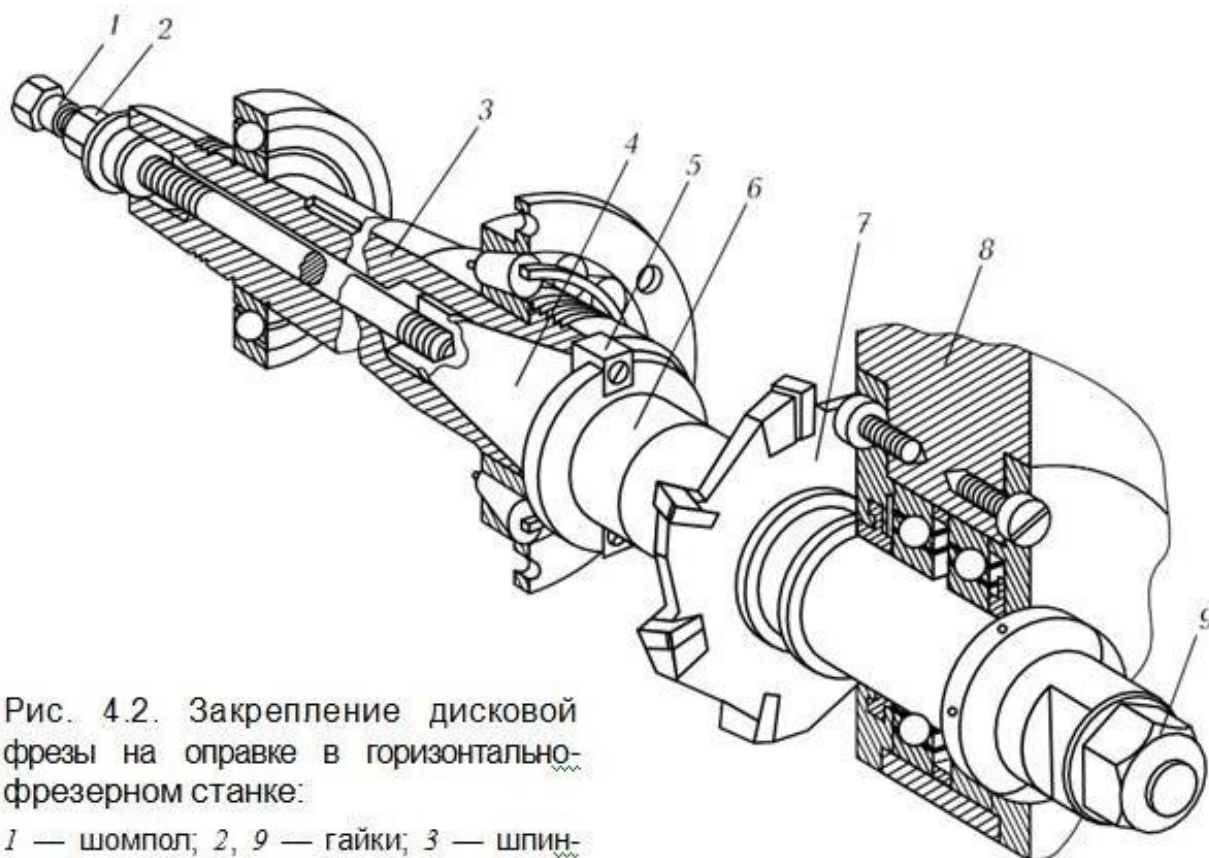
Закрепление дисковой фрезы на оправке в горизонтально-фрезерном станке:
